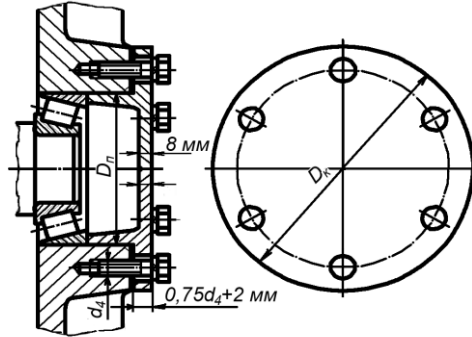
Основні конструктивні елементи корпусу і кришки традиційного типу (накладні кришки підшипників)
